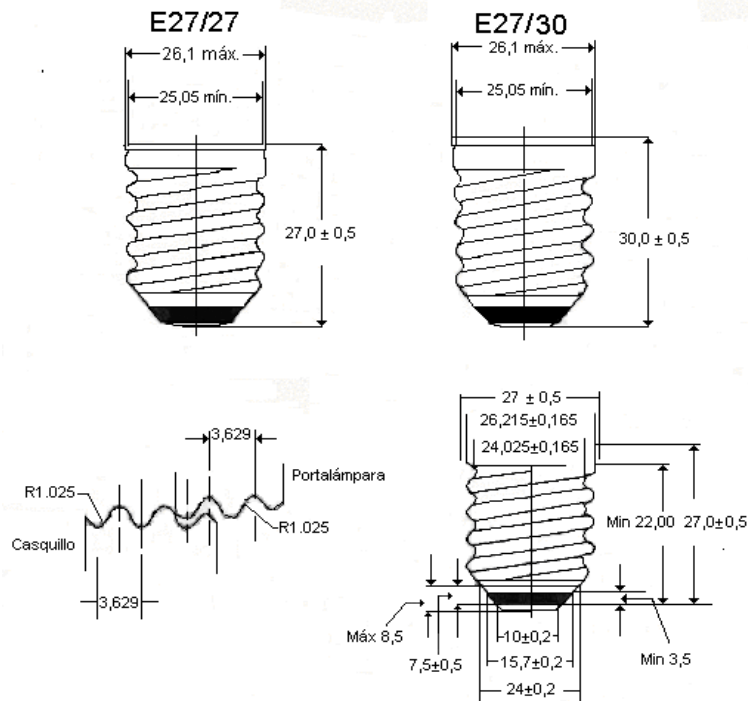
Dimensiones del casquillo de una bombilla en mm.
